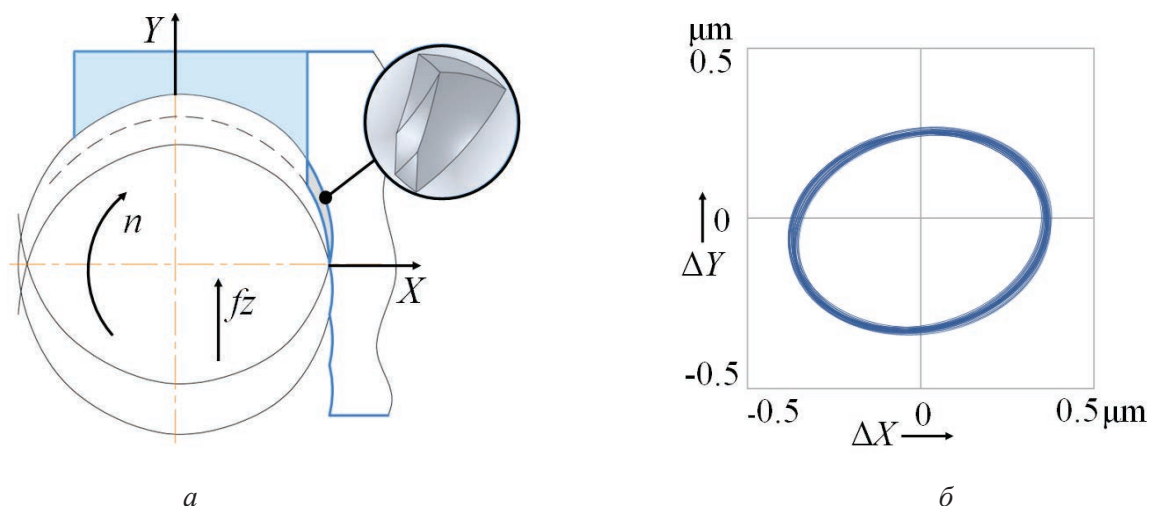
Схема прохождения режущих кромок фрезы через зону обработки:
